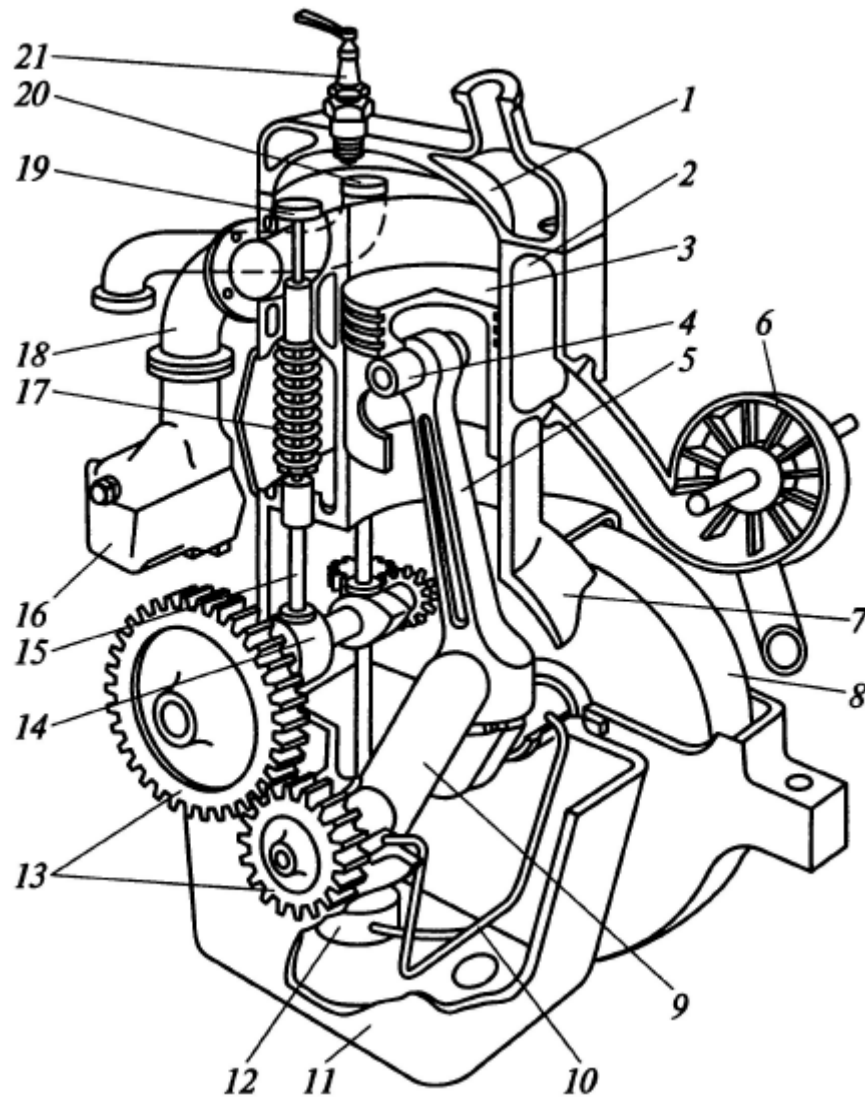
Устройство одноцилиндрового карбюраторного двигателя
